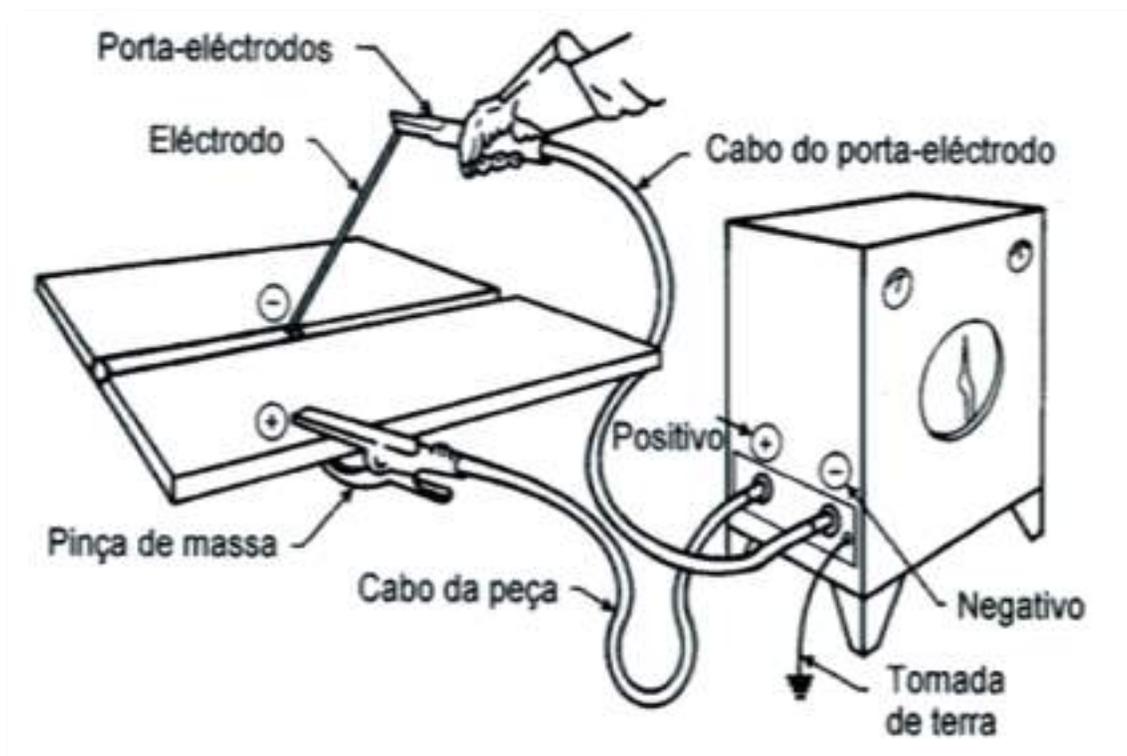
Esquema de uma instalação de soldadura por eléttodos revestidos.
